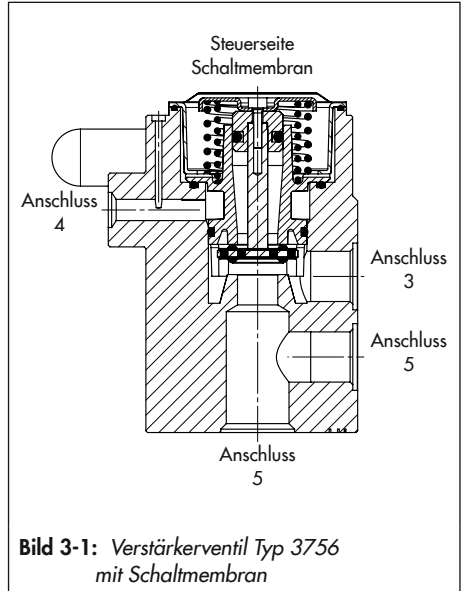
Verstärkerventil Typ 3756 mit Schaltmembran
